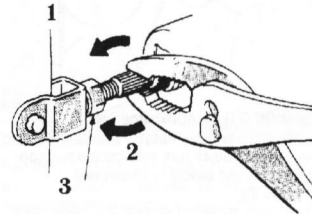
б Используйте плоскогубцы для поворачивания действующего рычага усилителя тормозов, чтобы отрегулировать высоту и свободный ход педали тормоза
